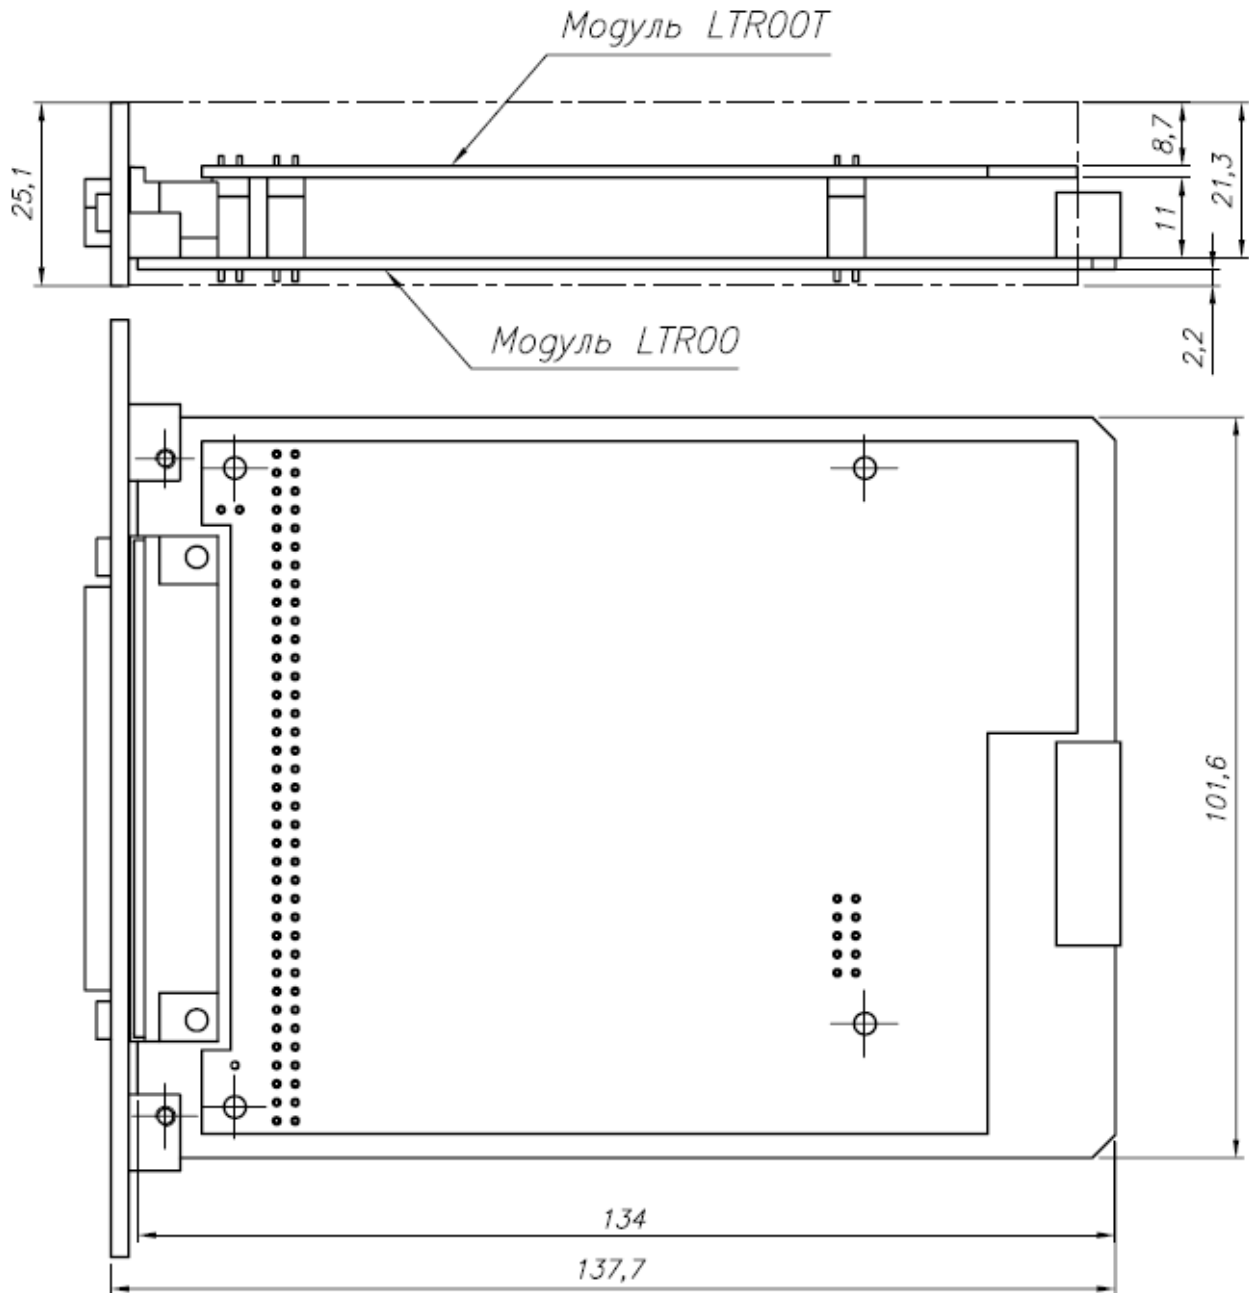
Чертёж модуля LTR00-01 в сборе с пользовательской печатной платой
